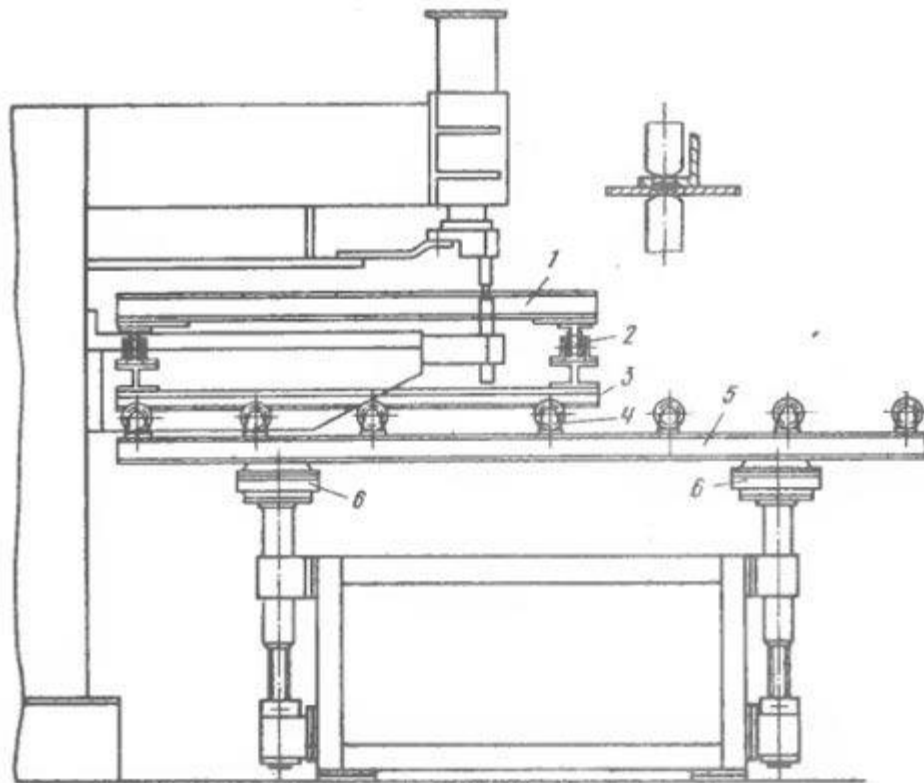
Приспособлення для точкового зварювання: 1 – рама;
